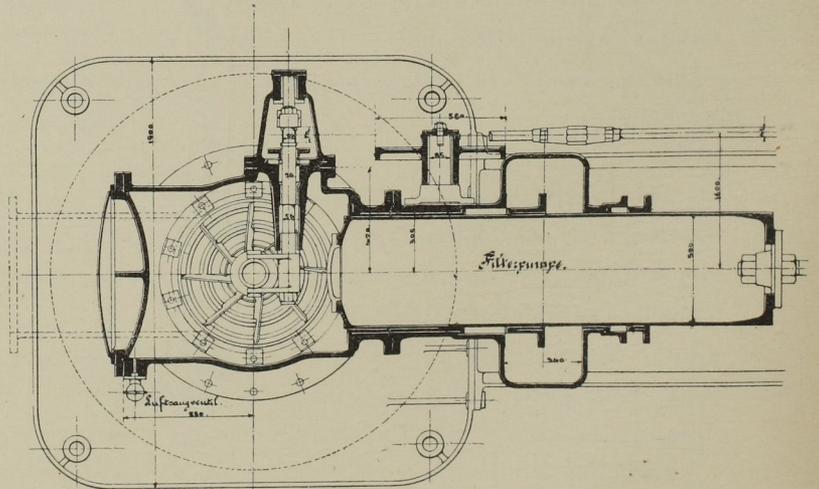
Grundriss der Filterpumpe. Massst. 1:30.
